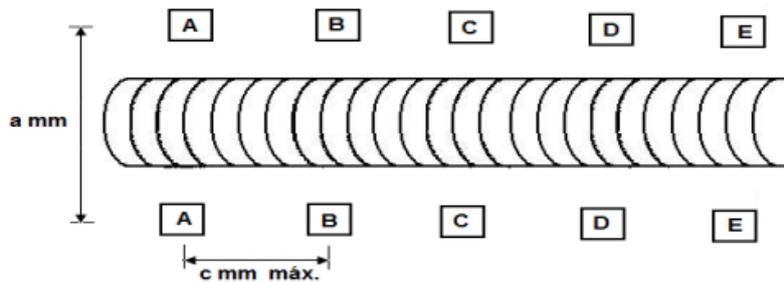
Soldas de Topo em Tubos, Posicionamento Longitudinal à Solda.
